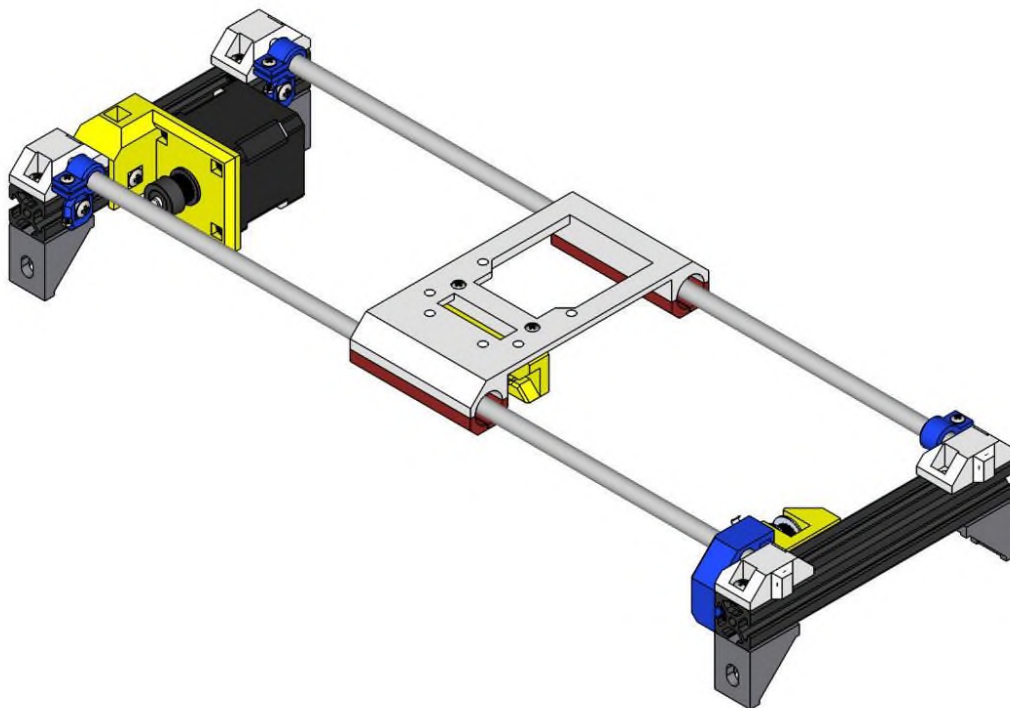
3D-модель конструкції механізму лінійного переміщення маніпулятора
